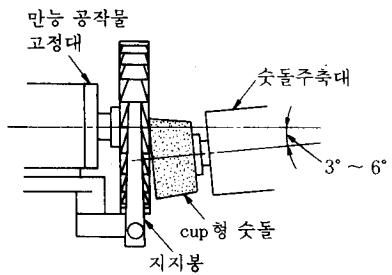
cup形 칫돌에 의한 side milling cutter의側面研削
